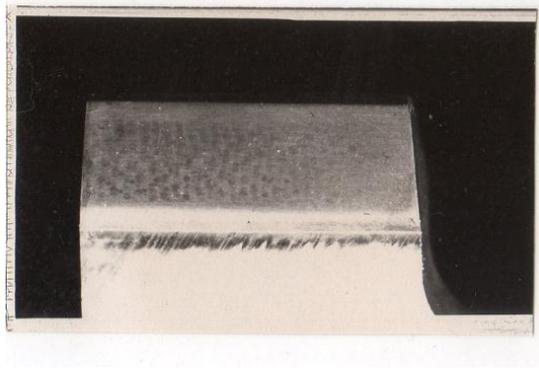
Внешний вид цилиндрических прижогов на рабочей поверхности зуба, образованных из-за неустойчивой работы упругой системы шлифовального станка
